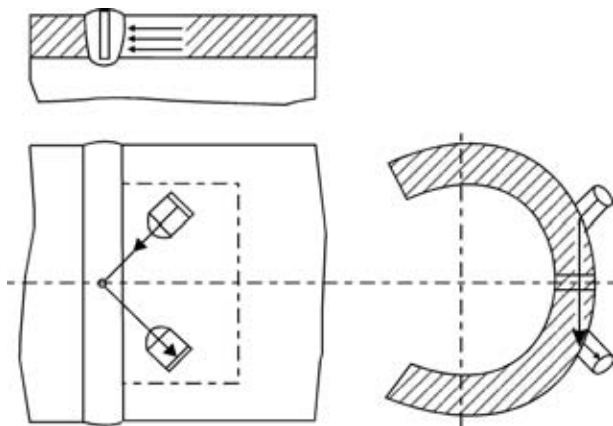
Схема УЗ контроля кольцевых сварных швов раздельно-совмещенными хордовыми преобразователями
